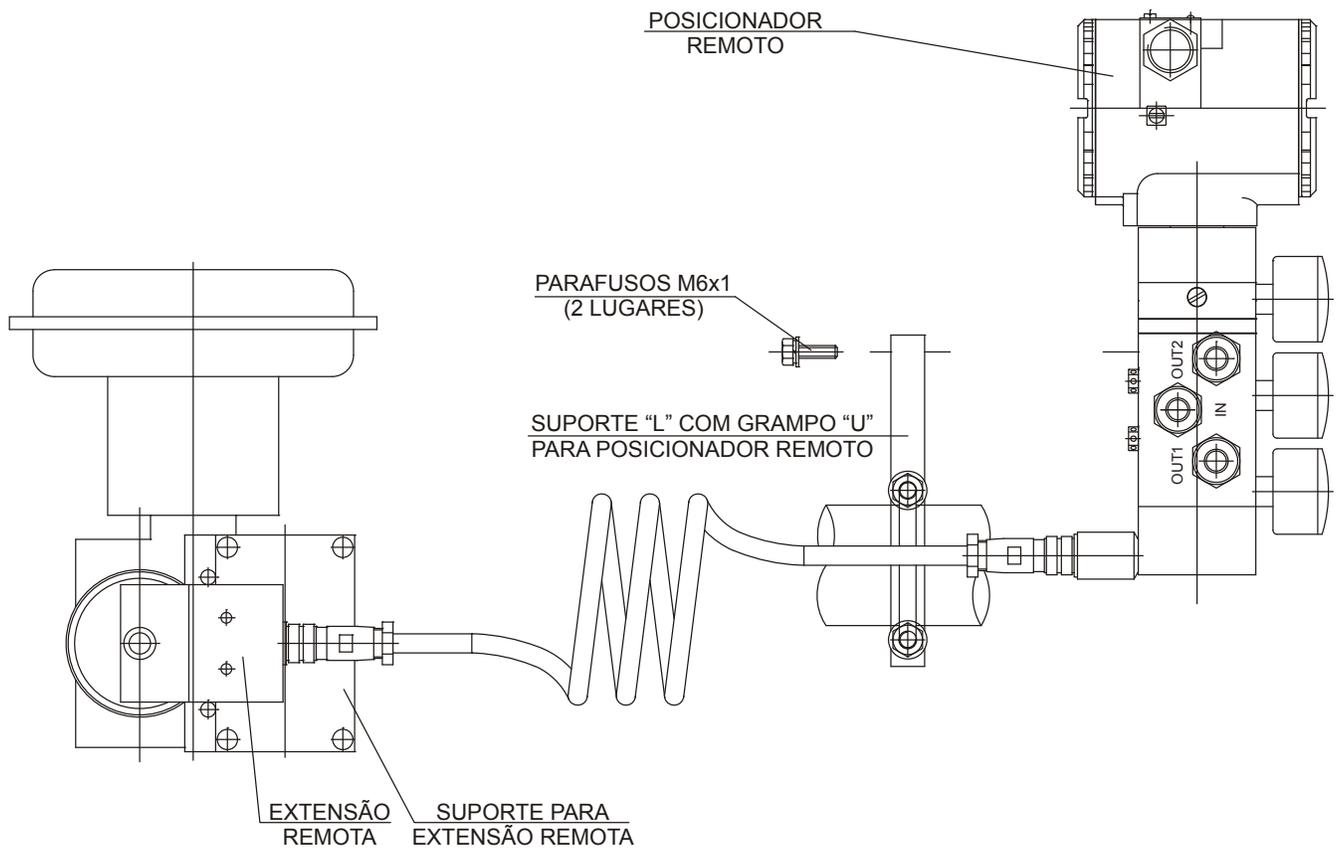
Posicionador em Atuador Rotativo com Sensor de Posição Remoto
